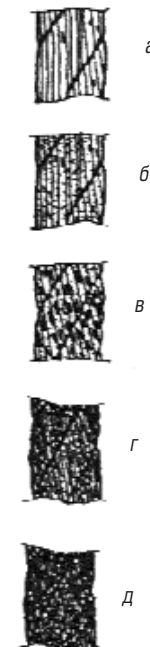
Поверхнева корозія дротів каната хрестової звивки:
